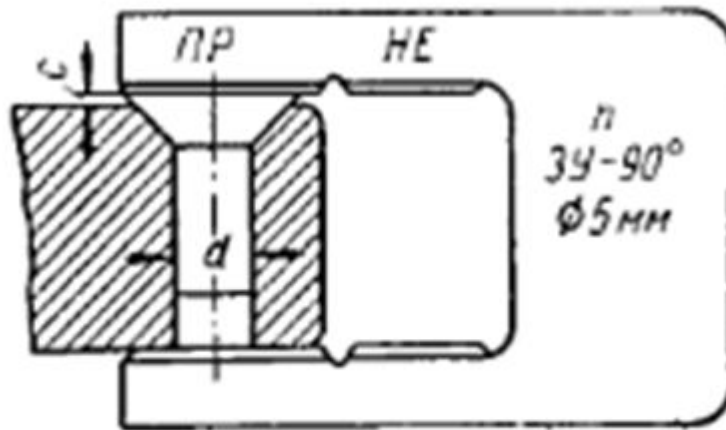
Предельный калибр-скоба и державка для контроля высоты головки заклепки.
